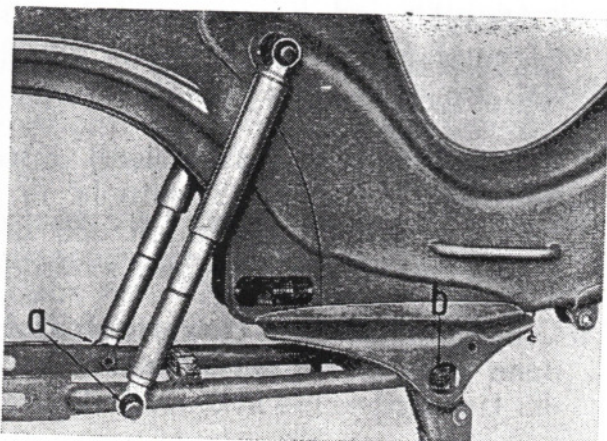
Befestigung des hinteren Schwingarmes VI/57/858
